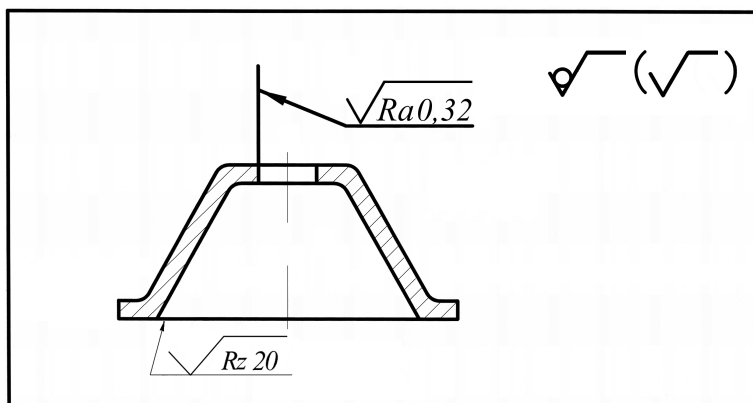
Обозначение шероховатости для детали, имеющей необработанные поверхности
